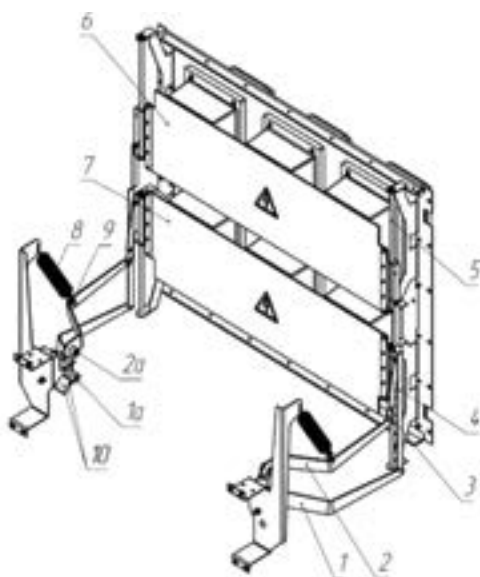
Шторочный механизм шкафов с выключателями на номинальные токи 2000-4000 А
